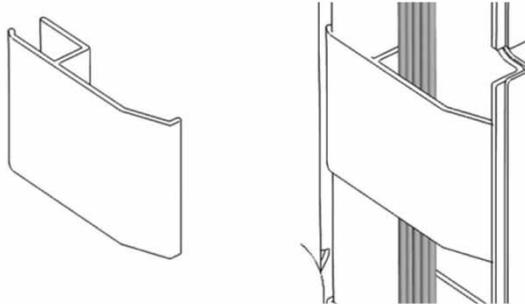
Schlauchklammer (links); Schlauchklammer installiert (rechts)
